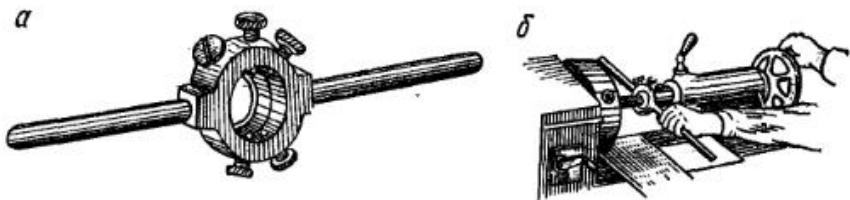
Нарезание резьбы с креплением плашки в слесарном плашкодержателе
